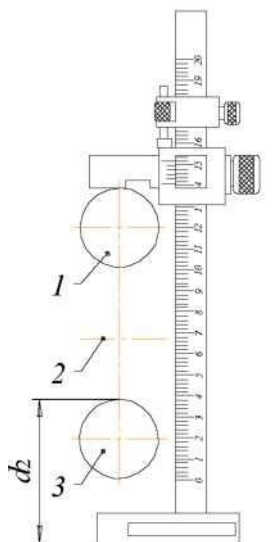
Штангенрейсмус: 1 - верхнє положення шийки; 2 - вісь обертання планшайби; 3 - нижнє положення шийки
